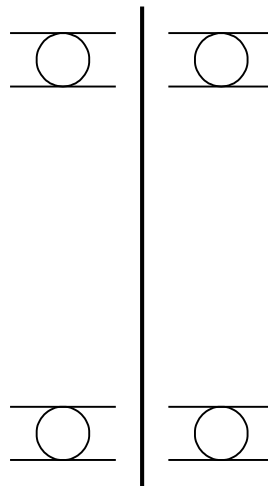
Конструктивна схема шпиндельного вузла на підшипниках кочення
